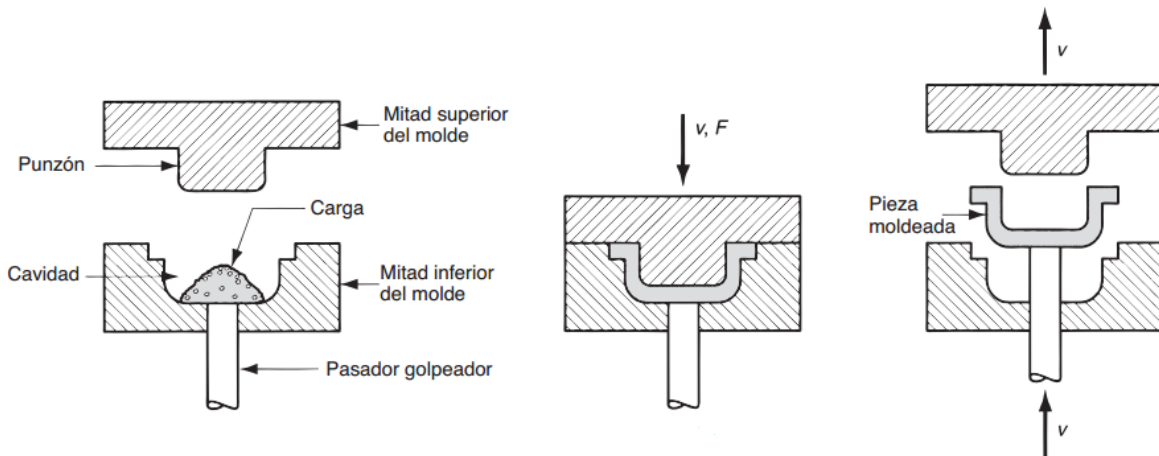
Proceso de formado por compresión. Instalación del polímero en el molde, posteriormente compresión en caliente, y finalmente apertura del molde.
